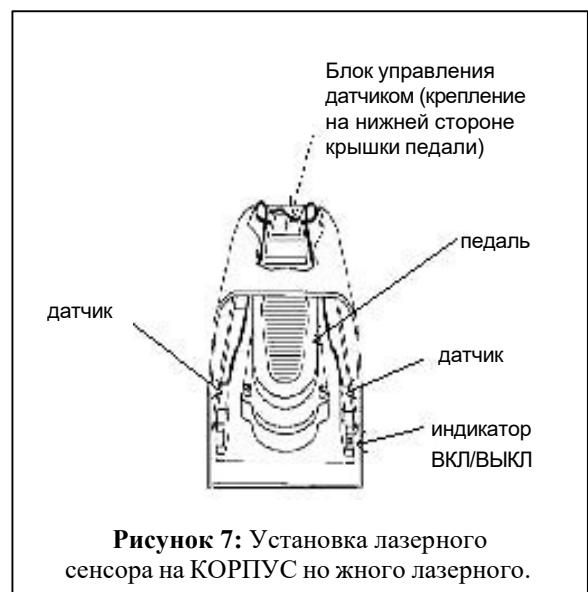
Установка лазерного сенсора на КОРПУС но жного лазерного.
